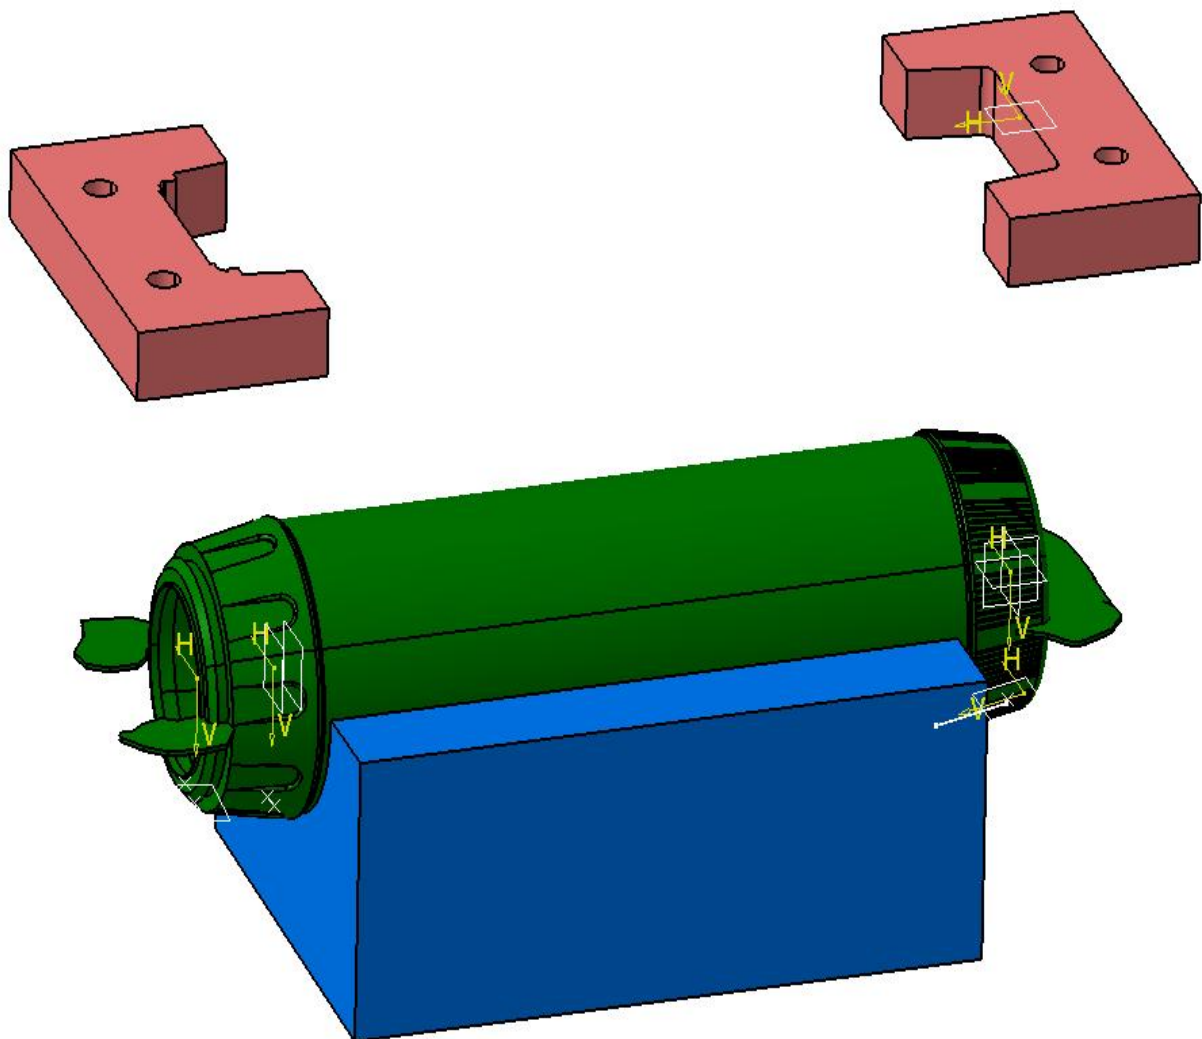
Detail zaploňování tvárníku a těsnících vložek
